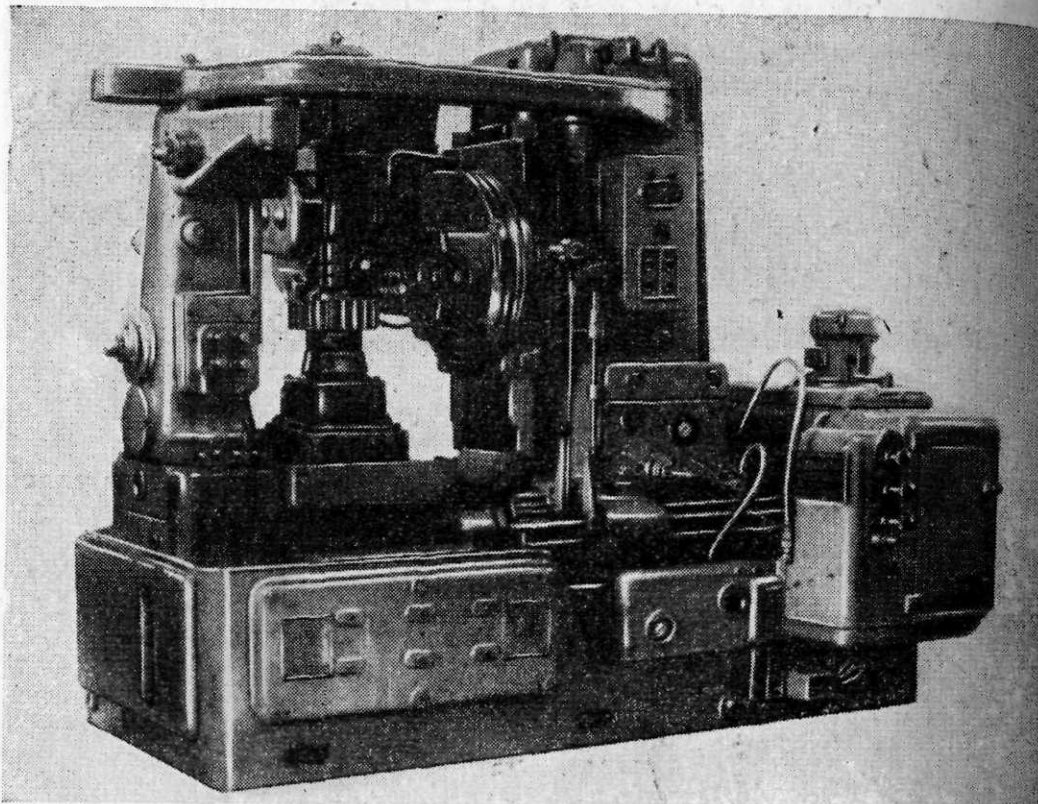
Зубофрезерный станок мод. 5Д32.
